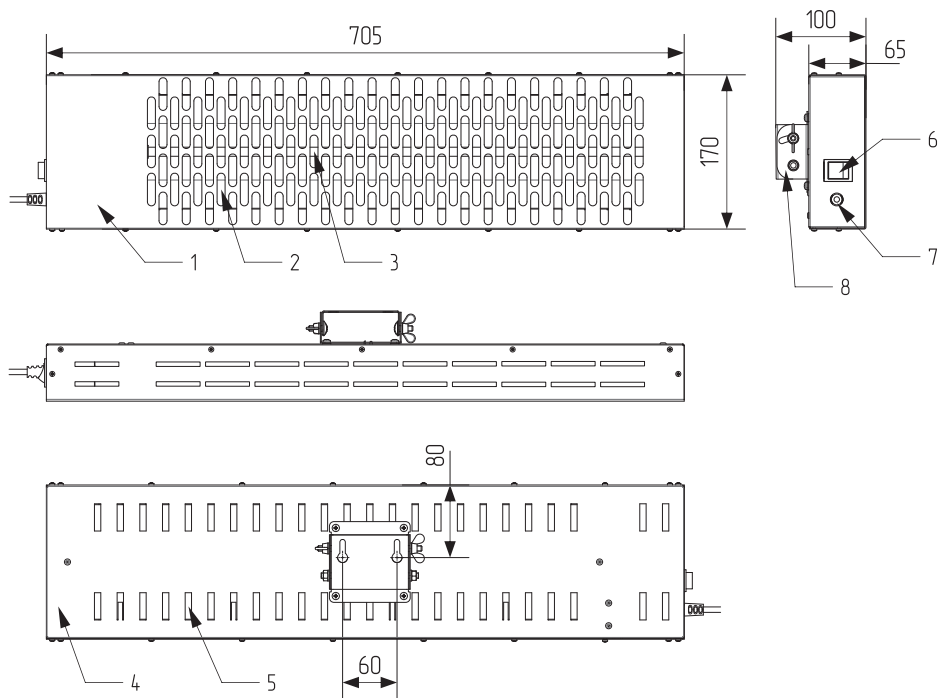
Габаритный чертёж и элементы конструкции электрического обогревателя «Пихта» СБИ-1000.
